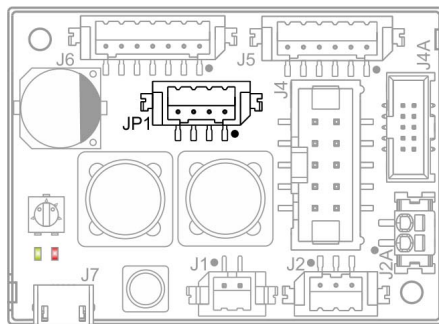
Steckbrücke JP1 – Einbauort
